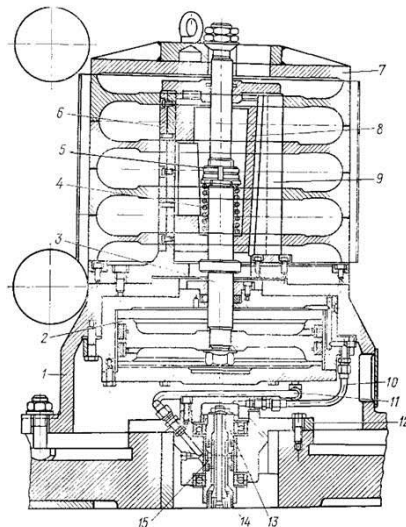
Пристосування з поршневим пневмоциліндром для фрезерування зубів у декількох циліндричних коліс
